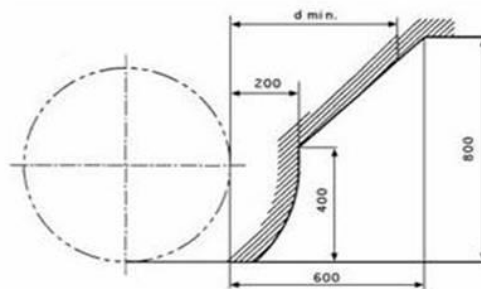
prospetto indicante le distanze di sicurezza tra la traiettoria degli utensili e il dispositivo di protezione incernierato - tratte dalla EN 708
